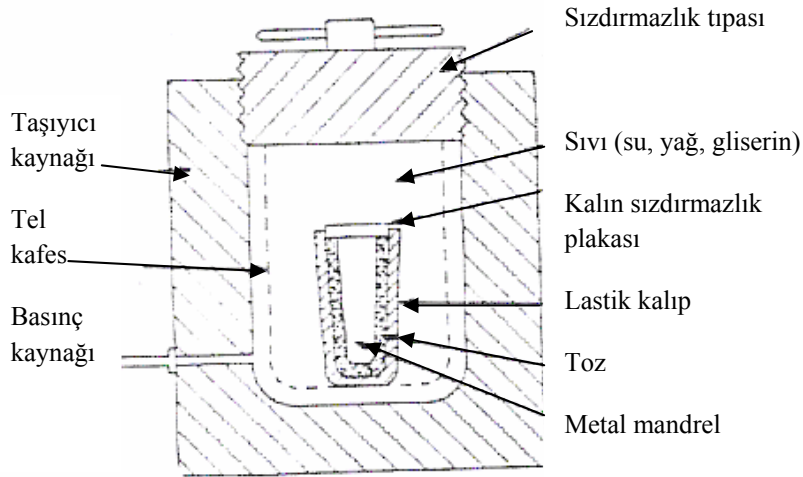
Metal tozu parçalarının presleme adımları [62]
